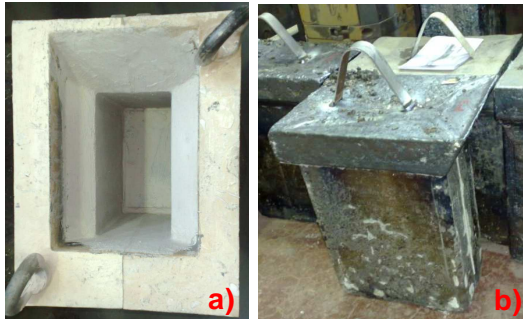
Molde real utilizado, a) Vista superior del molde y b) moldes con los lingotes solidificados.
